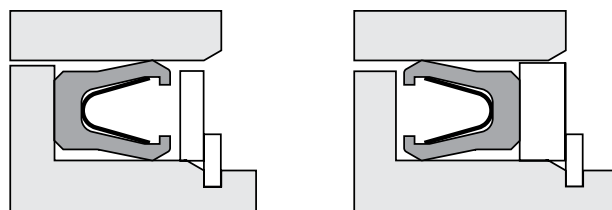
Посадочная канавка с фиксатором упорного кольца: установка «задней кромкой вперед» и «губками вперед»
